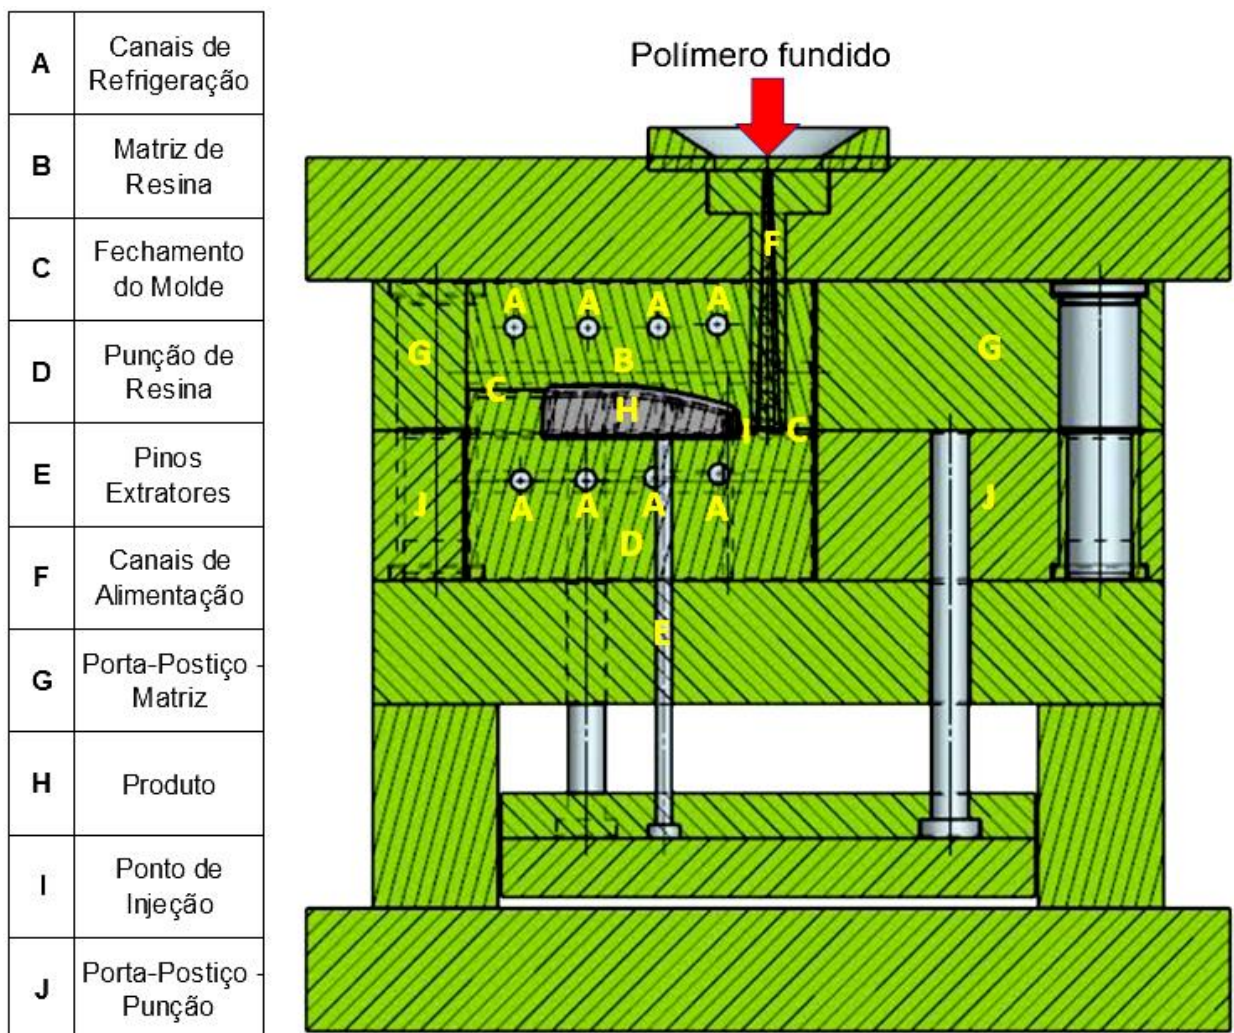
Ilustração do molde mecânico híbrido montado em corte.
